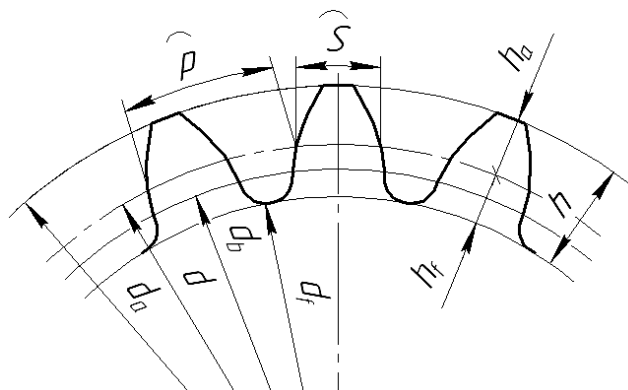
Геометрические параметры эвольвентного зубчатого колеса
